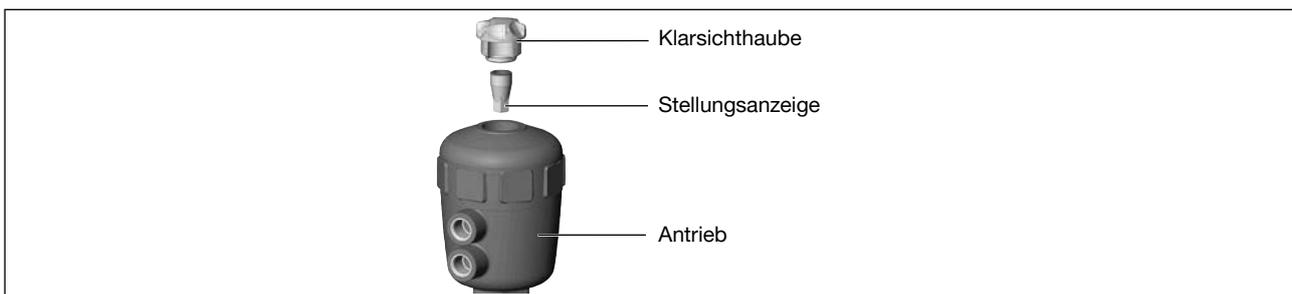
Schaltspindel montieren (1), externe Steuerluftführung
